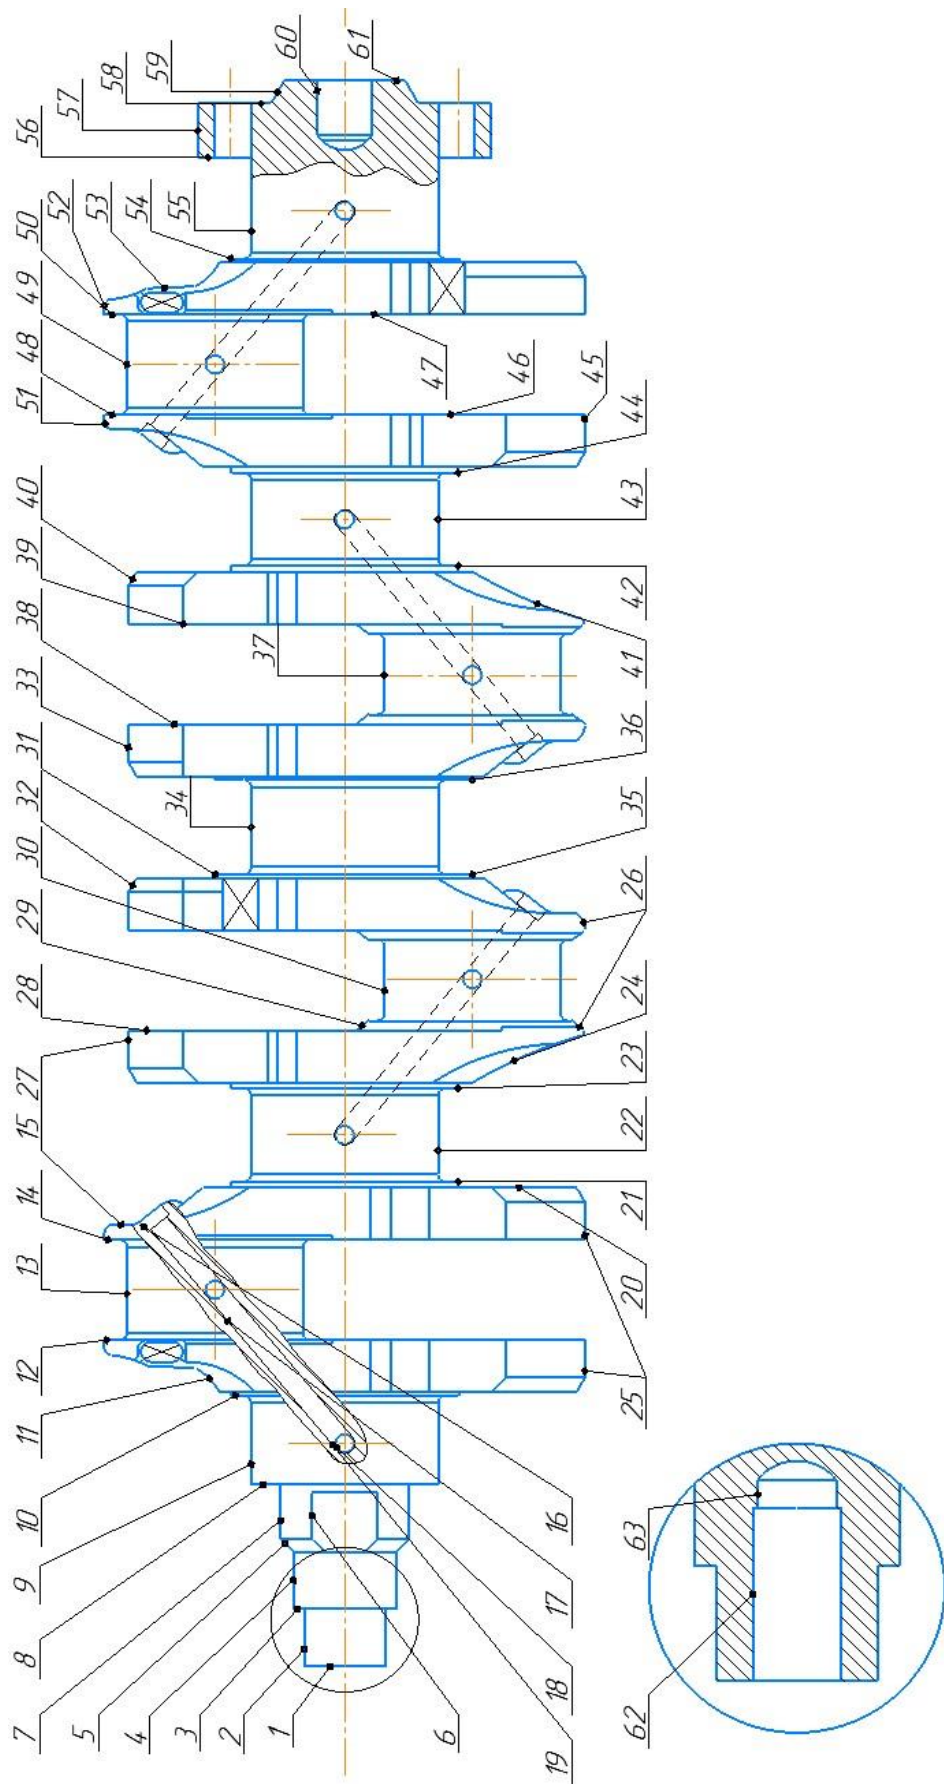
Общий вид чертежа детали - «Коленвал»
